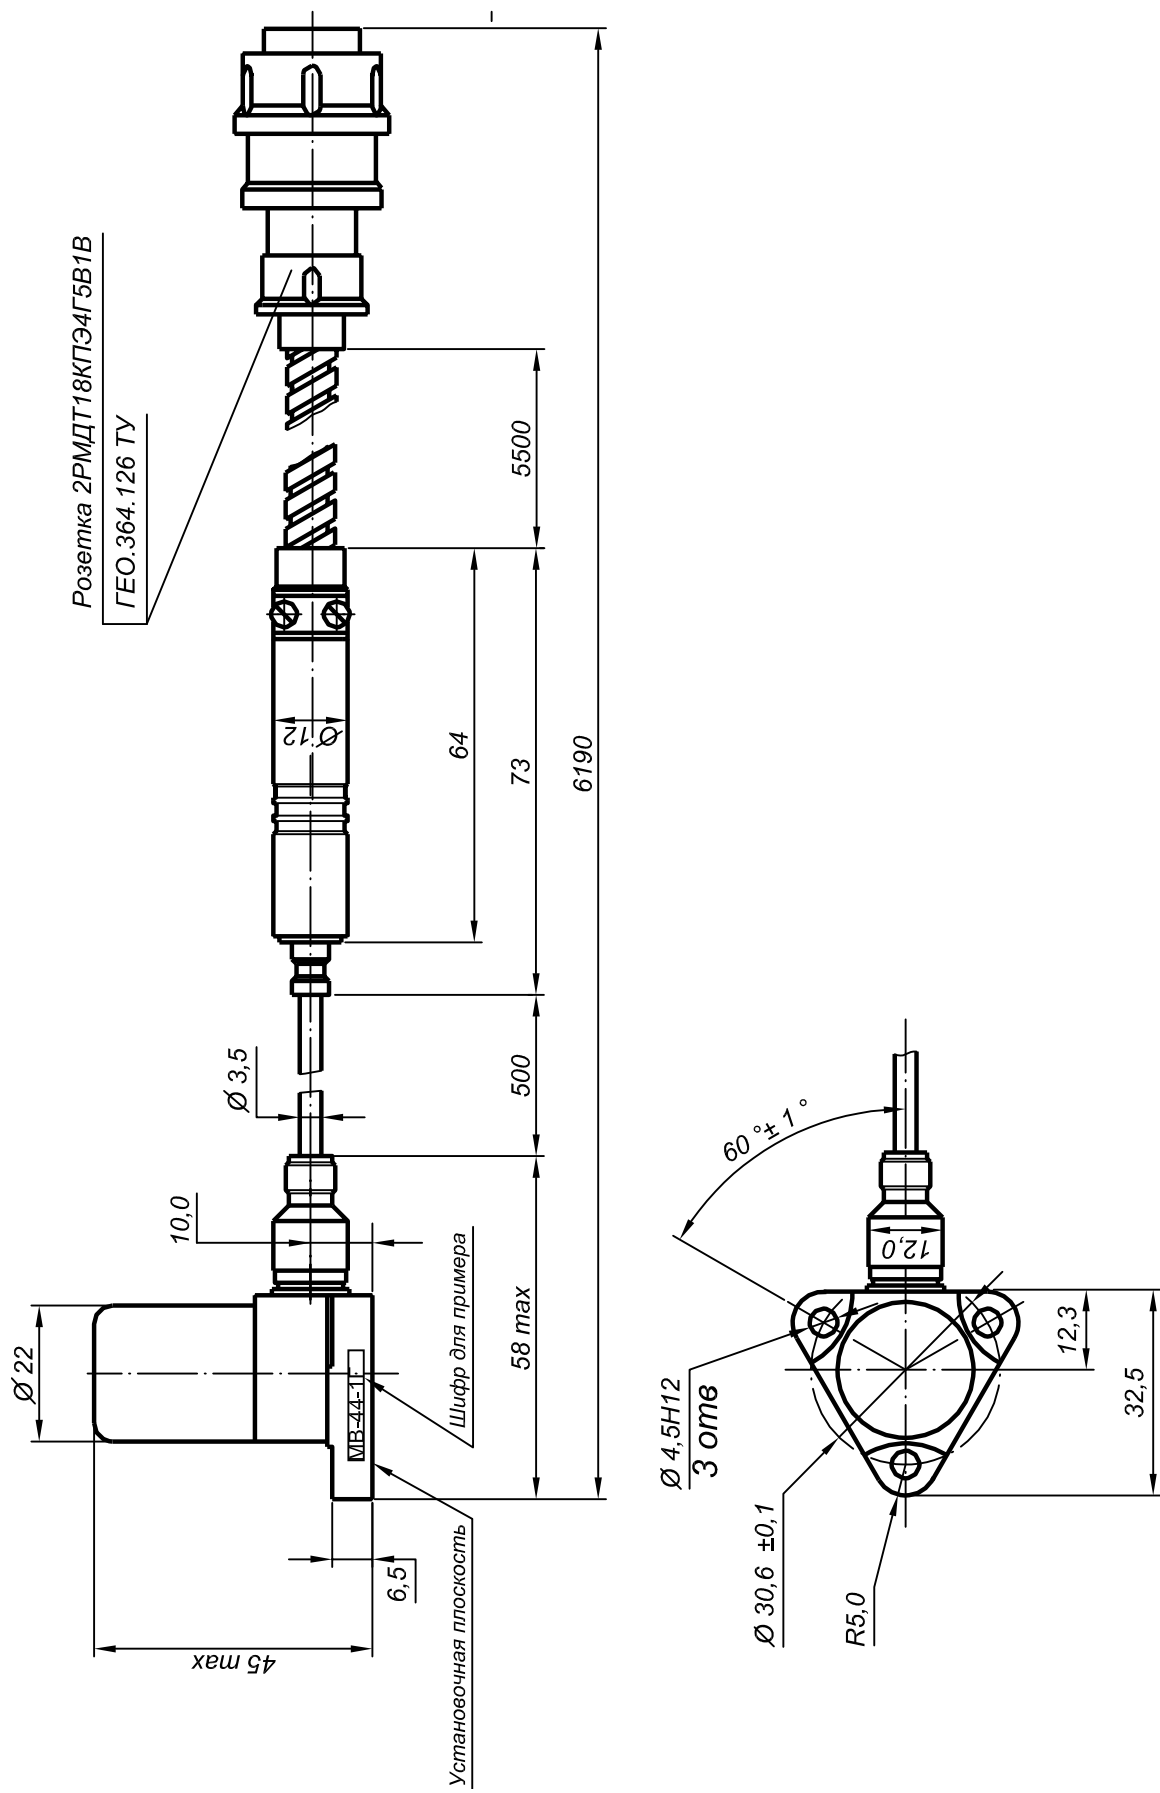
Габаритно-установочные размеры вибропреобразователя MB-44-1Г/0,5/5,5
